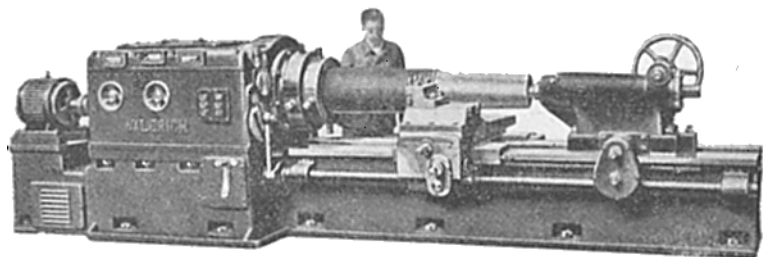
„Dr. Waldrich“, sestavy soustruhů.
